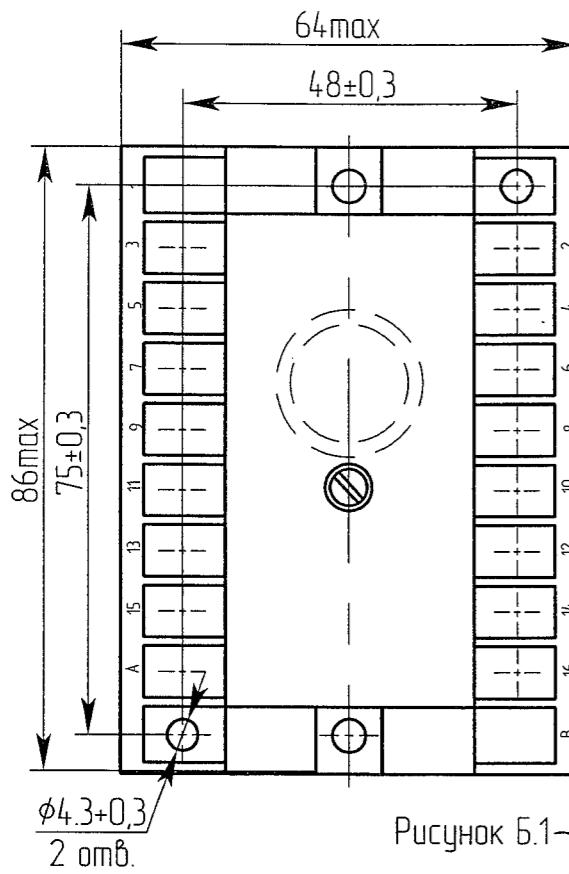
Реле типов PCB18-11-XXXX1, PCB-12-XXXX1,
